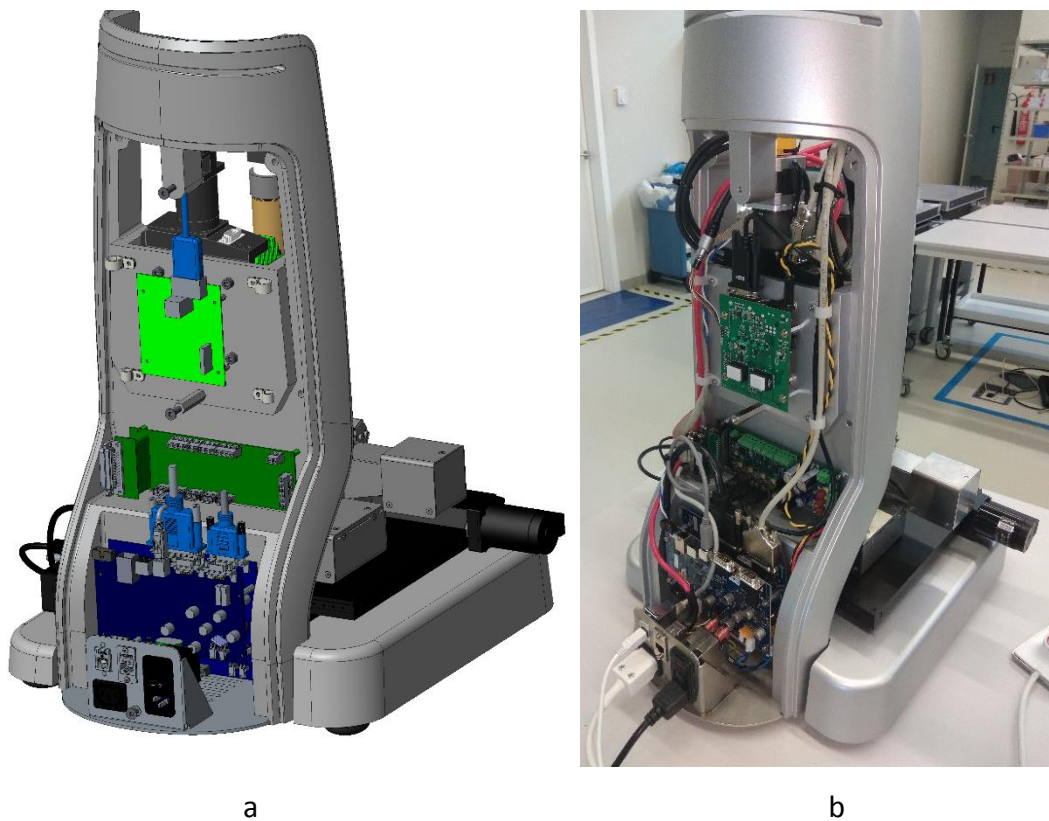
Vista de fons de l'instrument, (a) Disseny 3D, (b) construcció del primer prototip
